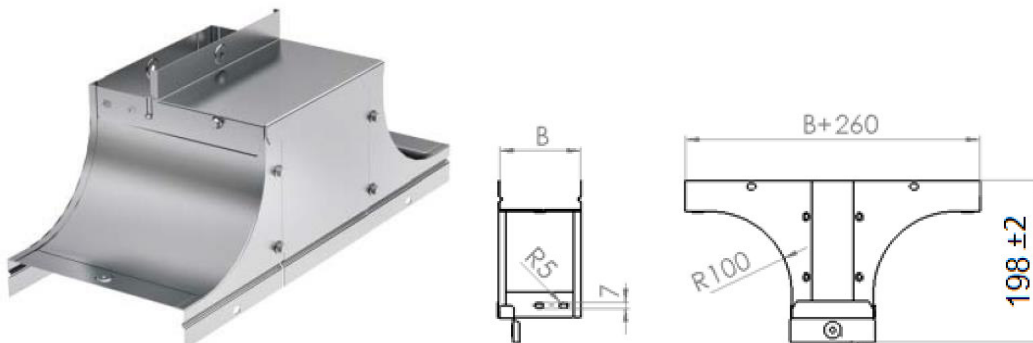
Крышка-ответвитель TSS, типов: 3753, 3723, 3722, 3733
